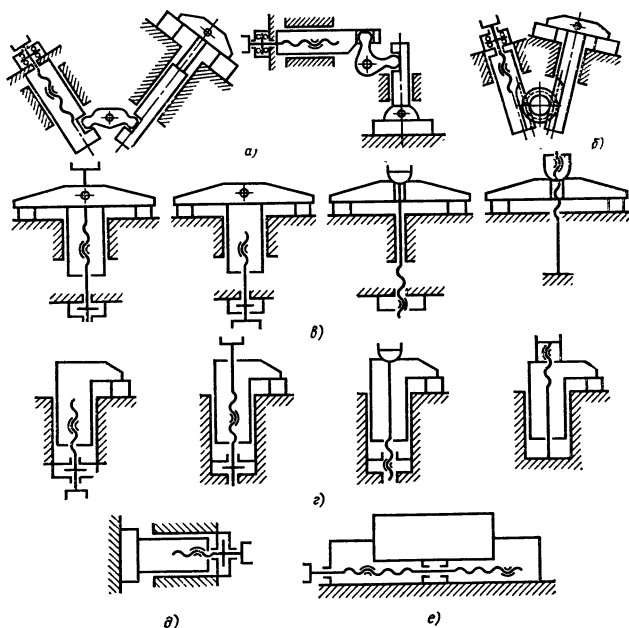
Схемы зажимных устройств приспособлений с приводом от электро- или гидромеханического ключа:
